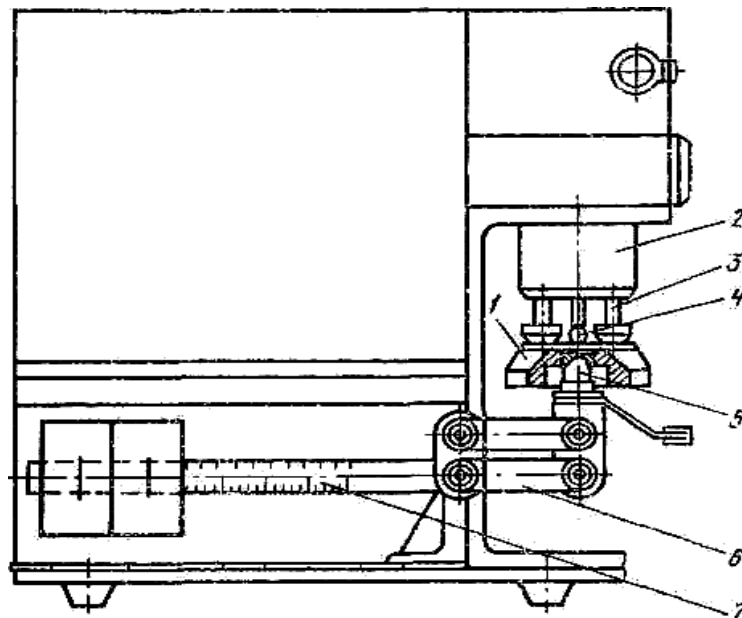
Конструктивная схема прибор ДИТ-М
